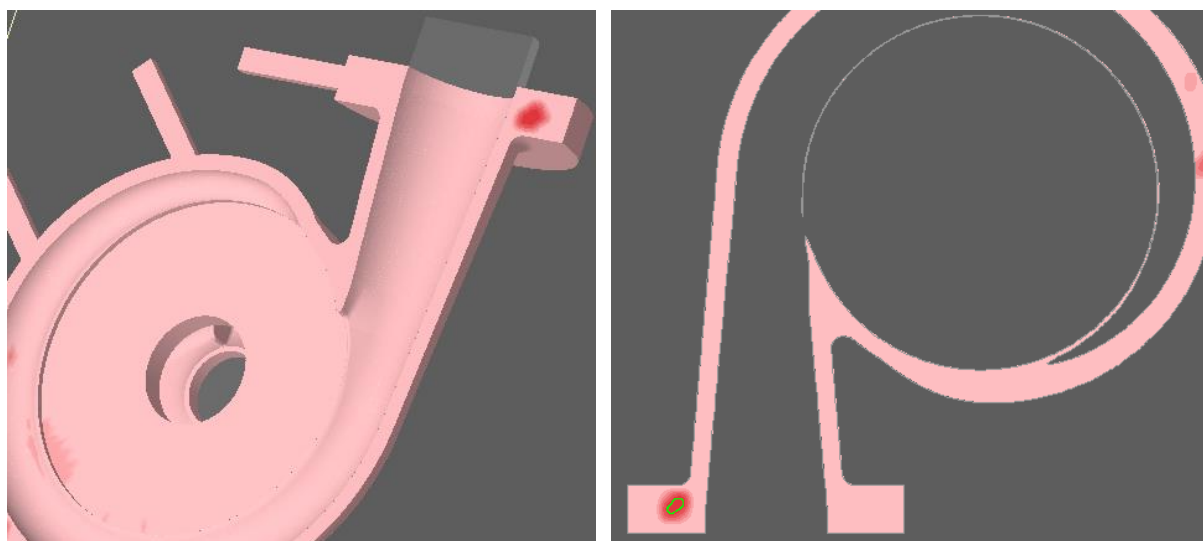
Усадочные дефекты в отливке «Корпус насоса» (сечение)
